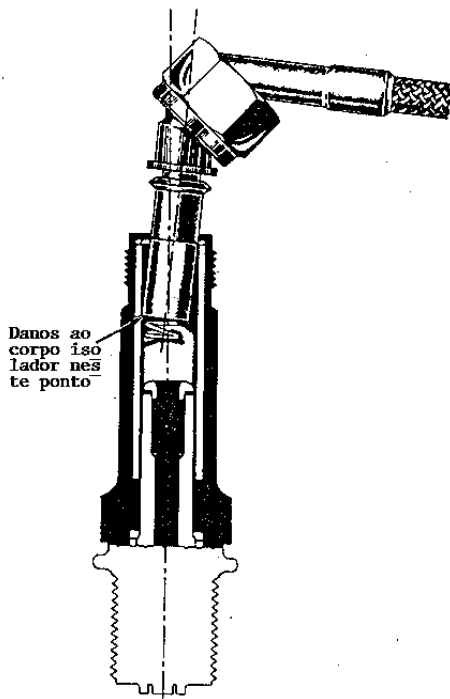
Técnica inadequada para remoção do cabo de vela.
